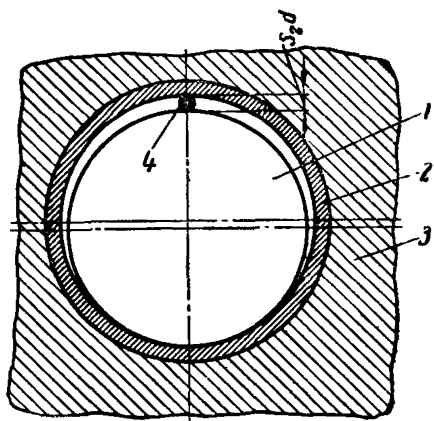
Способ контроля зазора в соединении вал — втулка:
